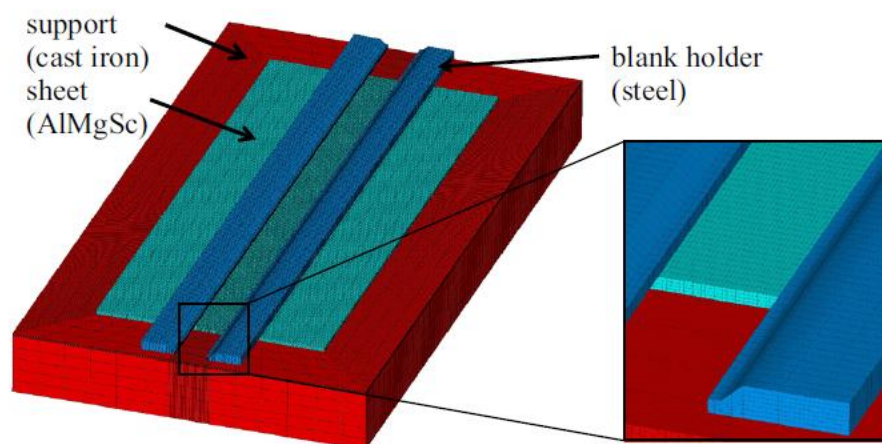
СЕ модель зразка зварного з'єднання з устаткуванням закріплення [12].
